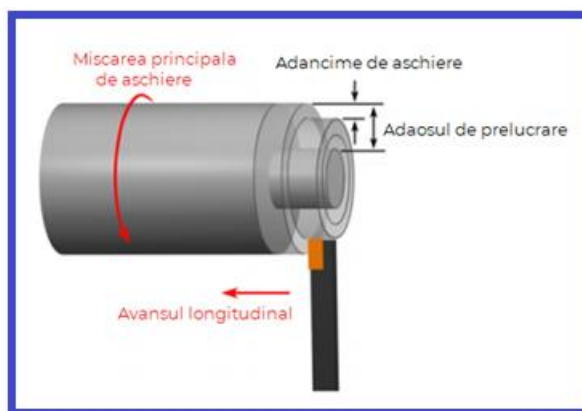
Strunjirea longitudinală exterioră (Tanase, 2019)
